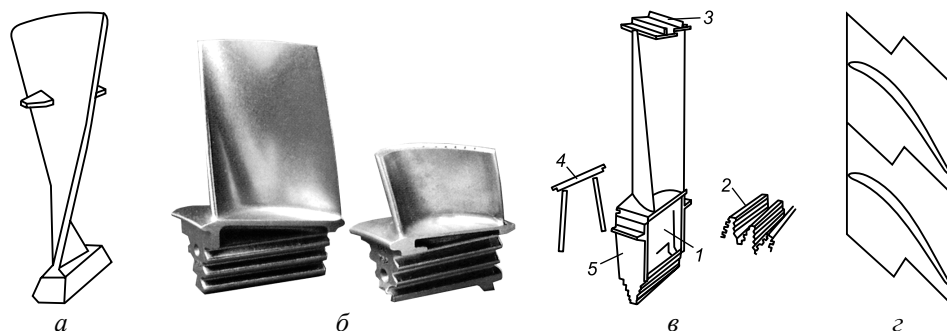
Рабочая лопатка осевого компрессора с демпферной связью (а), необандаженные рабочие лопатки турбины ГТУ PGT 2 (б), рабочая лопатка турбины с бандажной полкой и удлиненной ножкой (в) и вид сверху на z-образный стык бандажных полок (г): 1 – ножка лопатки; 2 – крепление хвостовика; 3 – бандажная полка; 4 – штифты уплотнения; 5 – уплотнение междискового пространства.
